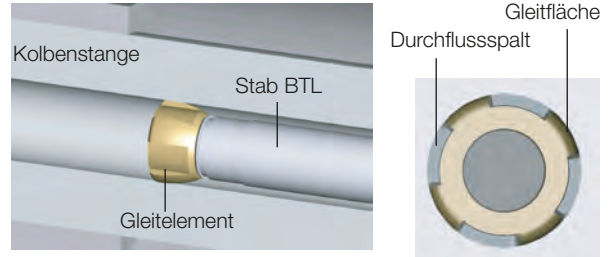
Detailansicht und Draufsicht Gleitelement
